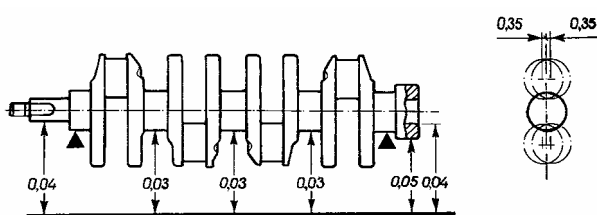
Допустимые биения основных поверхностей коленчатого вала
